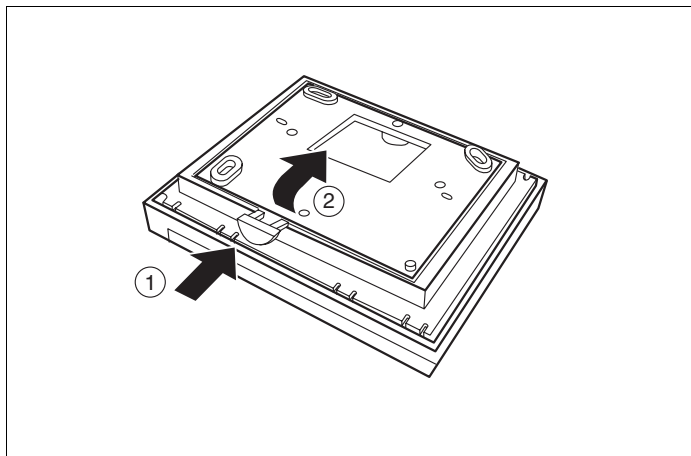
Se separă aparatul de reglaj de placa de montaj
